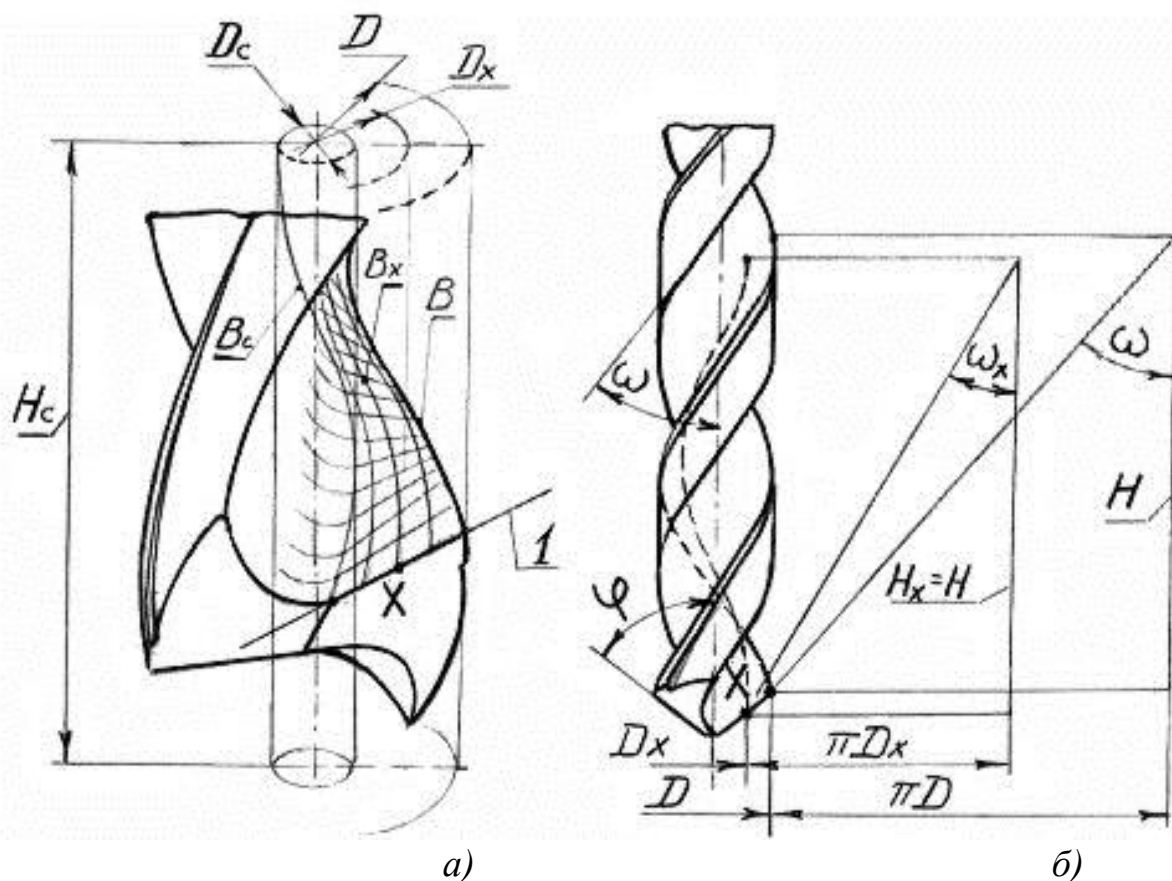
Схема формообразования передней поверхности и винтовой канавки спирального сверла:
